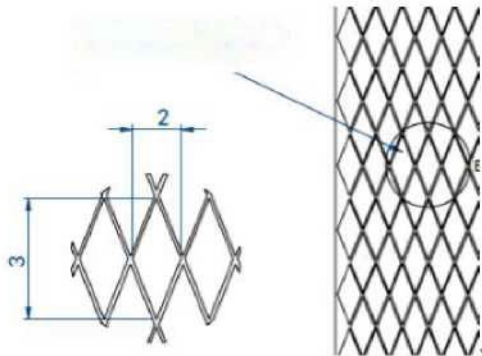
Эскиз сварной решетки передней/задней двери шкафа
